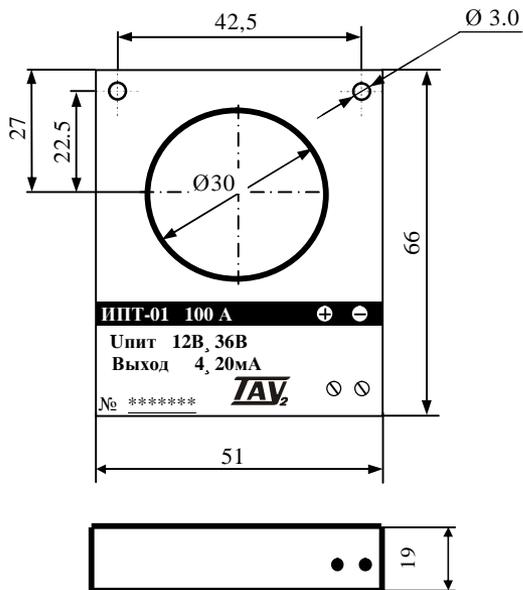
Габаритные размеры преобразователя тока измерительного ИПТ-01
